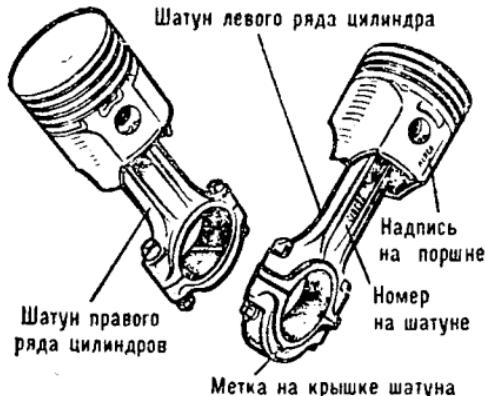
Установка двух шатунов на одной шатунной шейке V-образного двигателя
